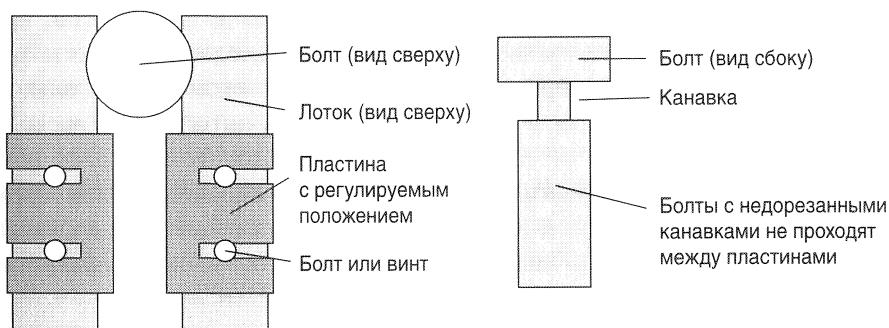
Устройство для отбраковки болтов с недорезанными канавками
